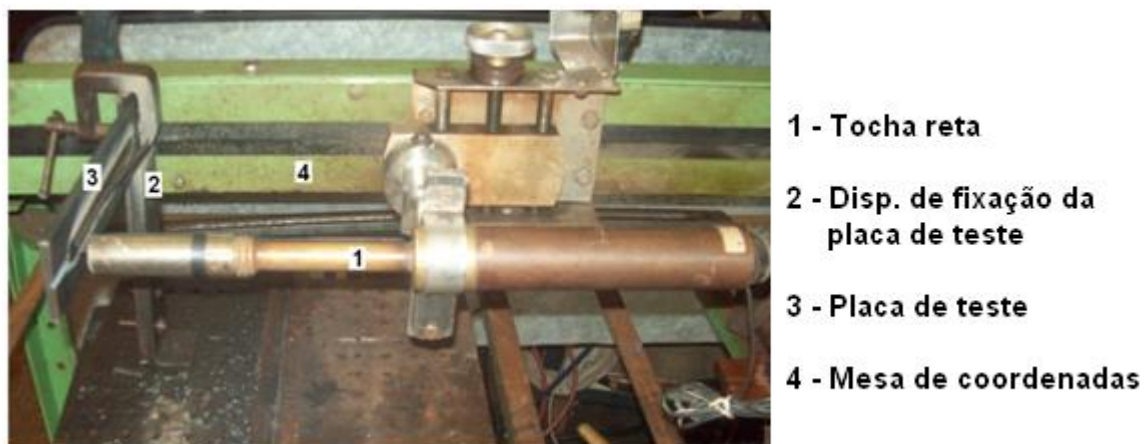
Conjunto: tocha reta, dispositivo de fixação, placa de teste e mesa coordenada.
